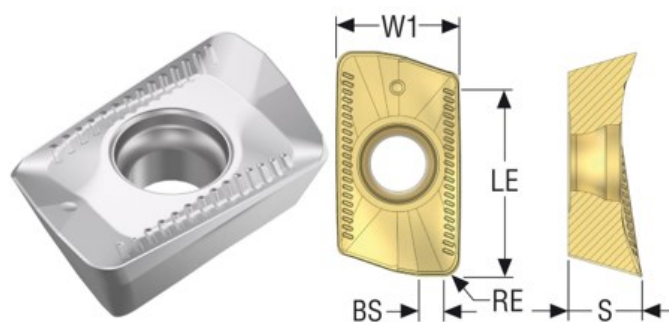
Fréza R217.69-0816.RE-10-2A
